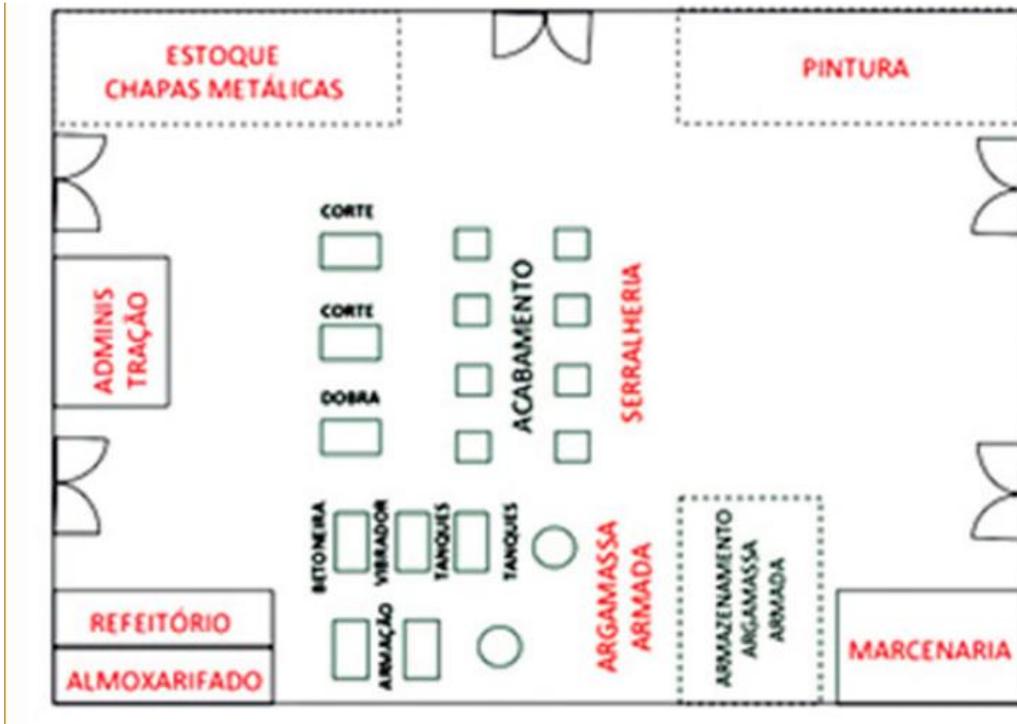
Layout esquemático da Fábrica de Equipamentos sociais de Ribeirão Preto. Fonte: Miysaka, 2002.
